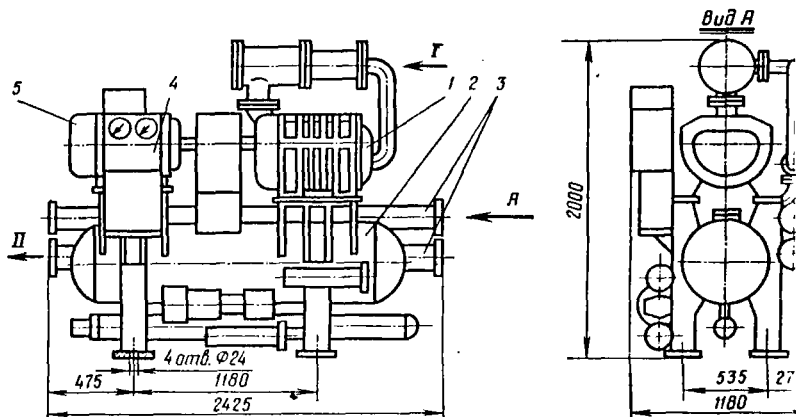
Установочные размеры компрессорного агрегата VX130-7-6 (АН130-7 винтовым компрессором:
